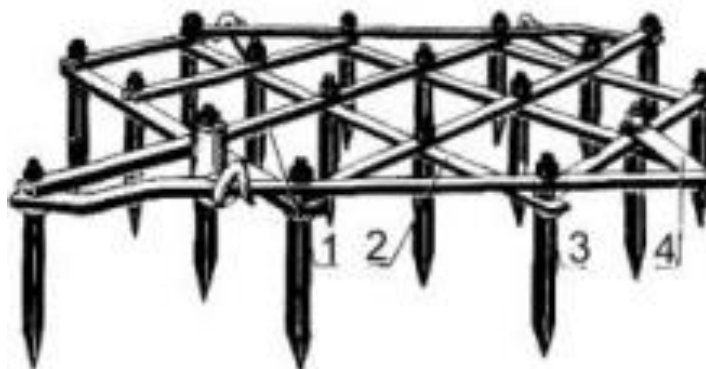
Зубова борона БЗТС-1,0: 1, 2 – планки; 3 – зуб; 4 – причіп
